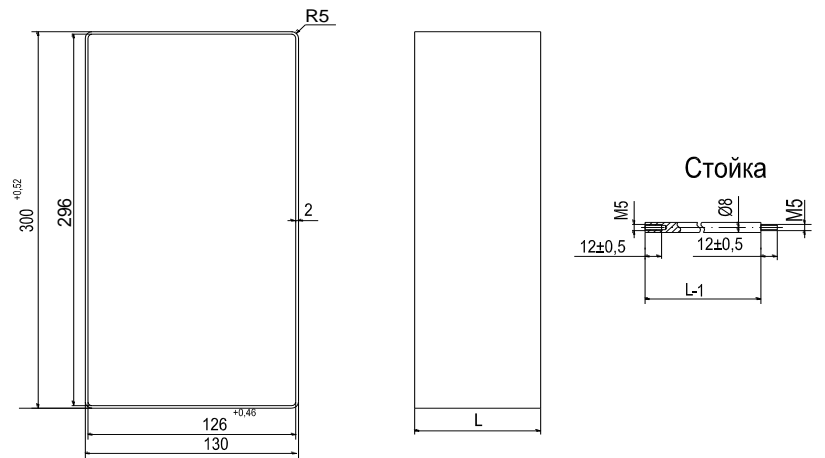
(лист 1 из 2) - Габаритные и установочные размеры
